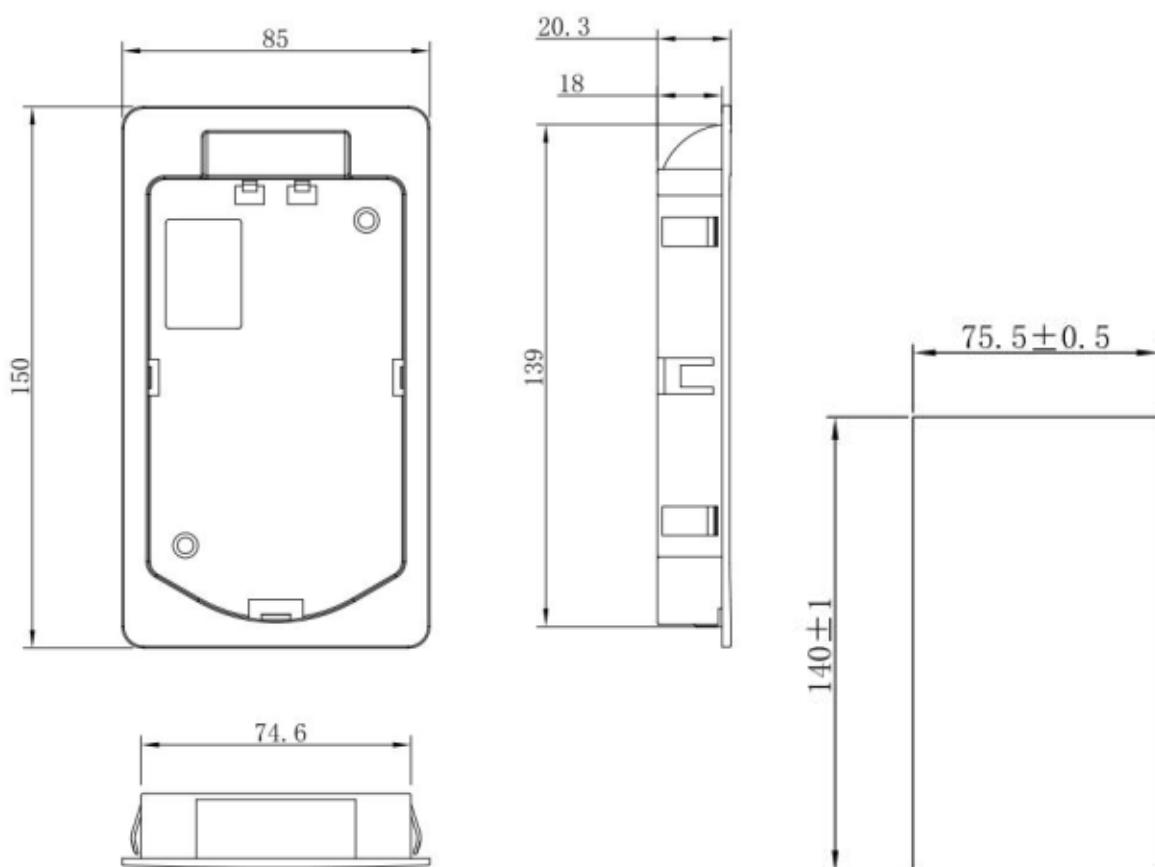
Габаритные размеры держателя кнопочной панели Keyboard bracket
